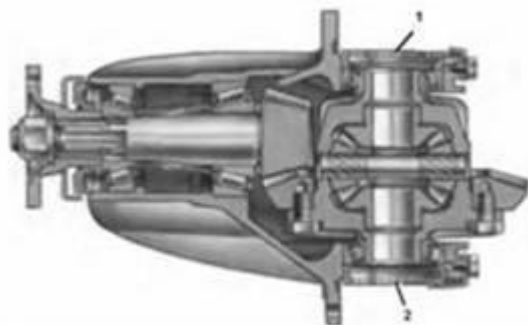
Схема для проверки предварительного натяга подшипников коробки дифференциала: D — расстояние между двумя крышками подшипников дифференциала; 1, 2 — регулировочные гайки.
